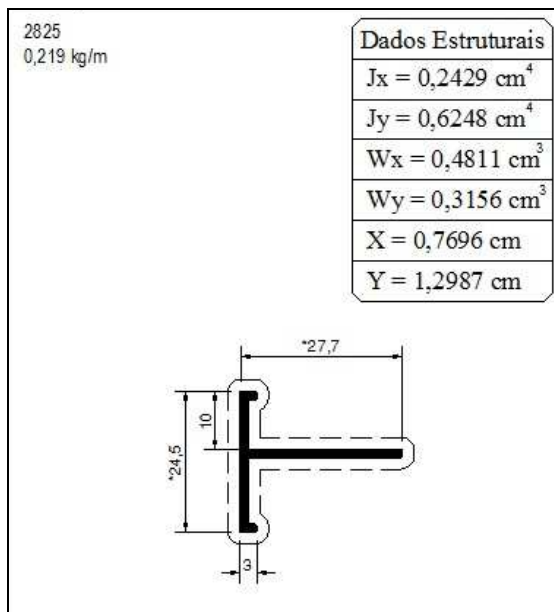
Perfil T de abas desiguais. Cotas em mm.
